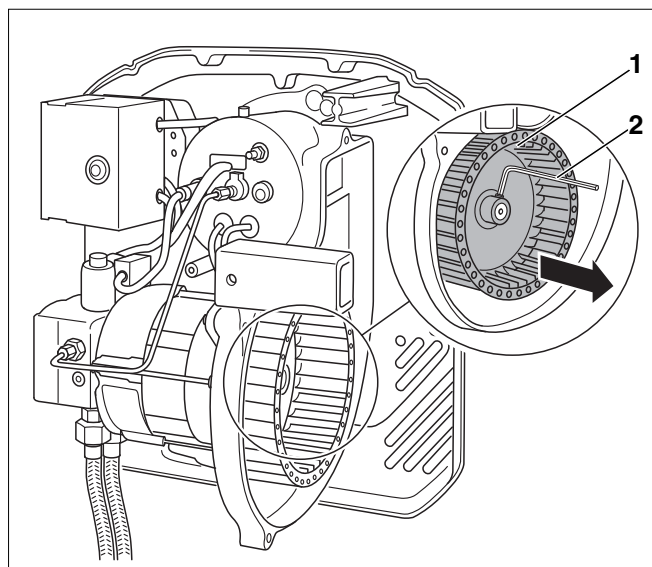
Comprobación y, dado el caso, limpieza de la turbina del ventilador
